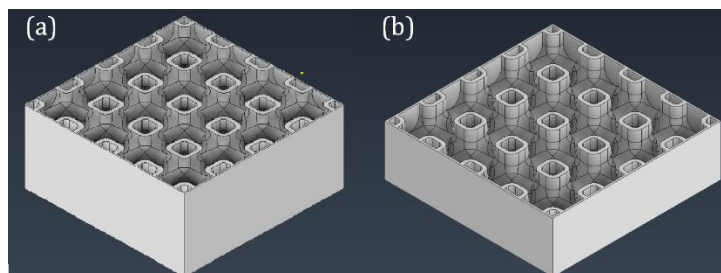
(a) Vista isométrica e (b) vista frontal do molde projetado.
